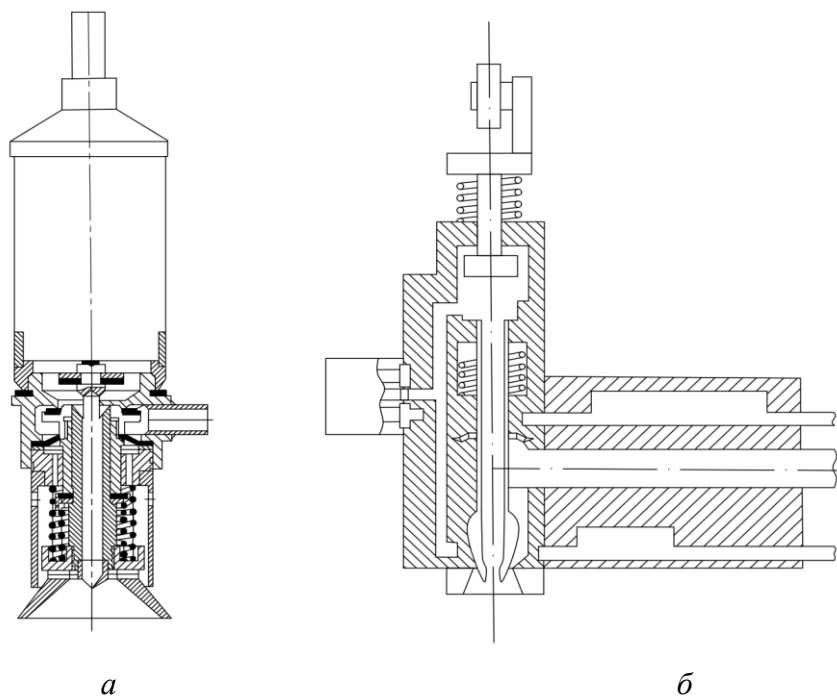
Креслення патрона: а – базовий; б – модернізований
